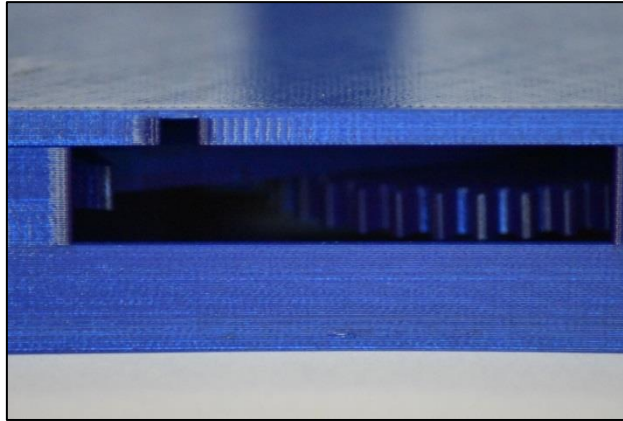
Detalle de la disposición en el interior del engranaje y el gancho.
